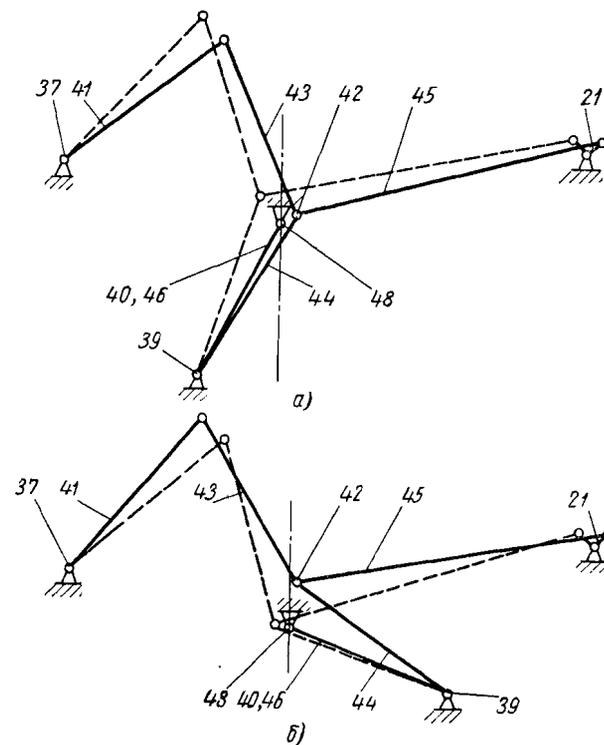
Схема механизма двигателя ткани машины 97-го класса
